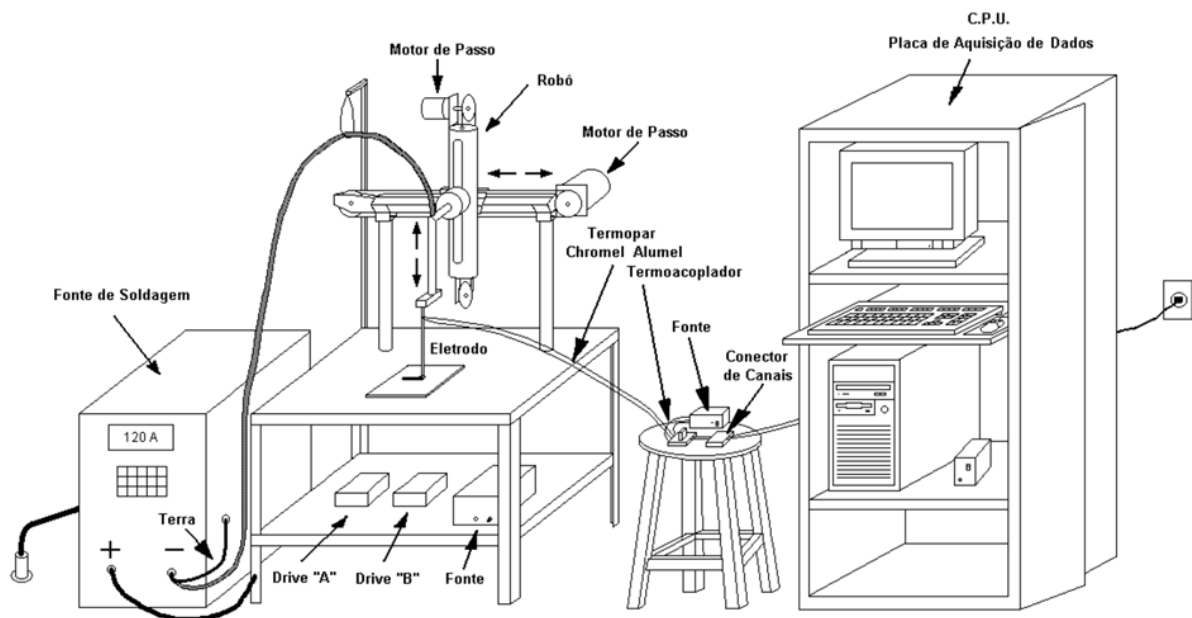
Sistema com manipulador de 2 GDL utilizado para soldagem com eletrodo revestido [Oliveira, 2000].
